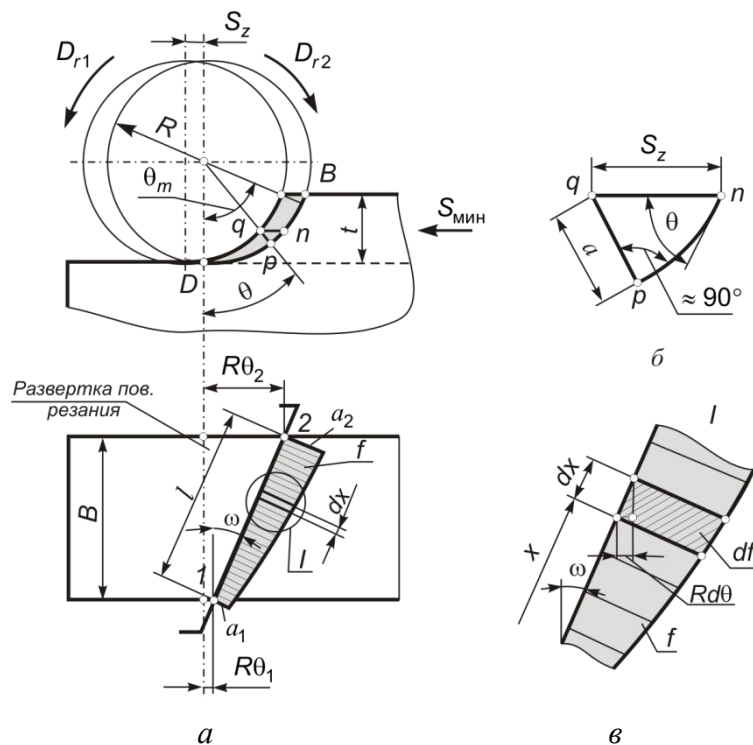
Элементы режима резания и параметры сечения срезаемого слоя при фрезеровании цилиндрическими фрезами
